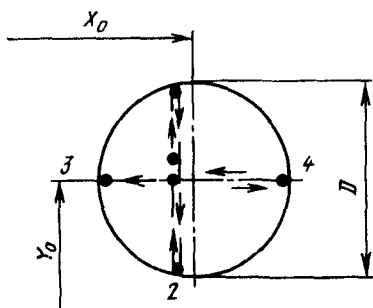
Схема относительного перемещения щупа контактной головки при измерении диаметра D отверстия и координат X_0 , Y_0 положения оси заготовки на многоцелевом станке
